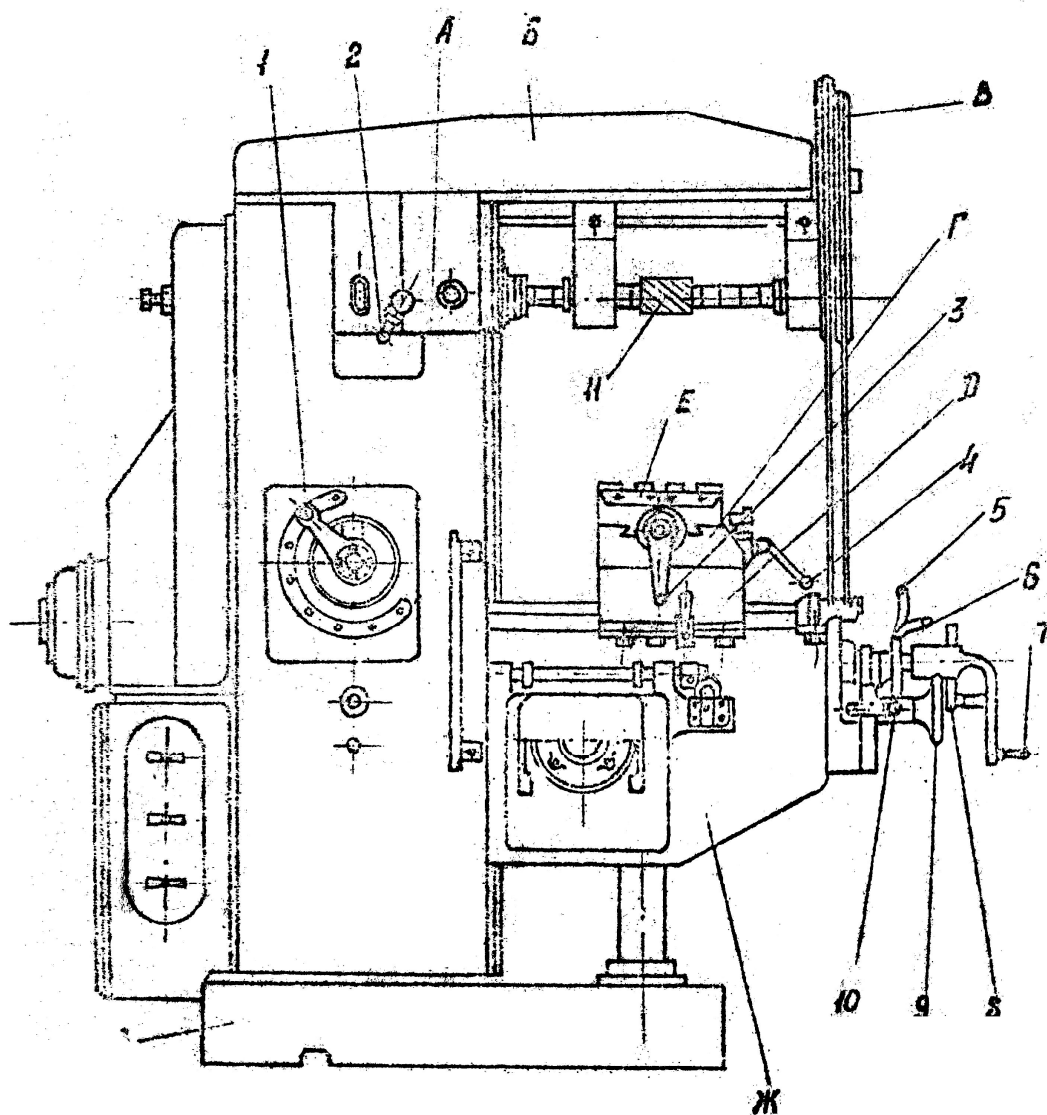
Загальний вигляд консольно-фрезерного верстата мод. 6Н81
